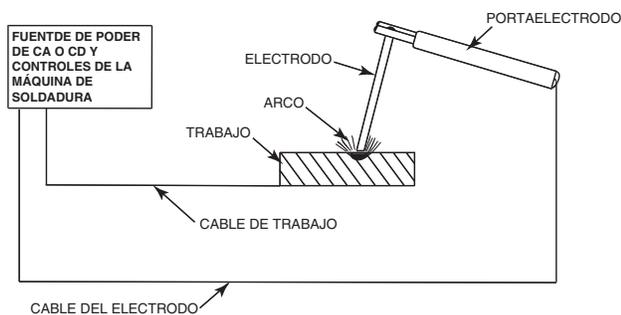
El circuito de soldadura para soldadura de arco metálico protegida (Electrodo Revestido).
